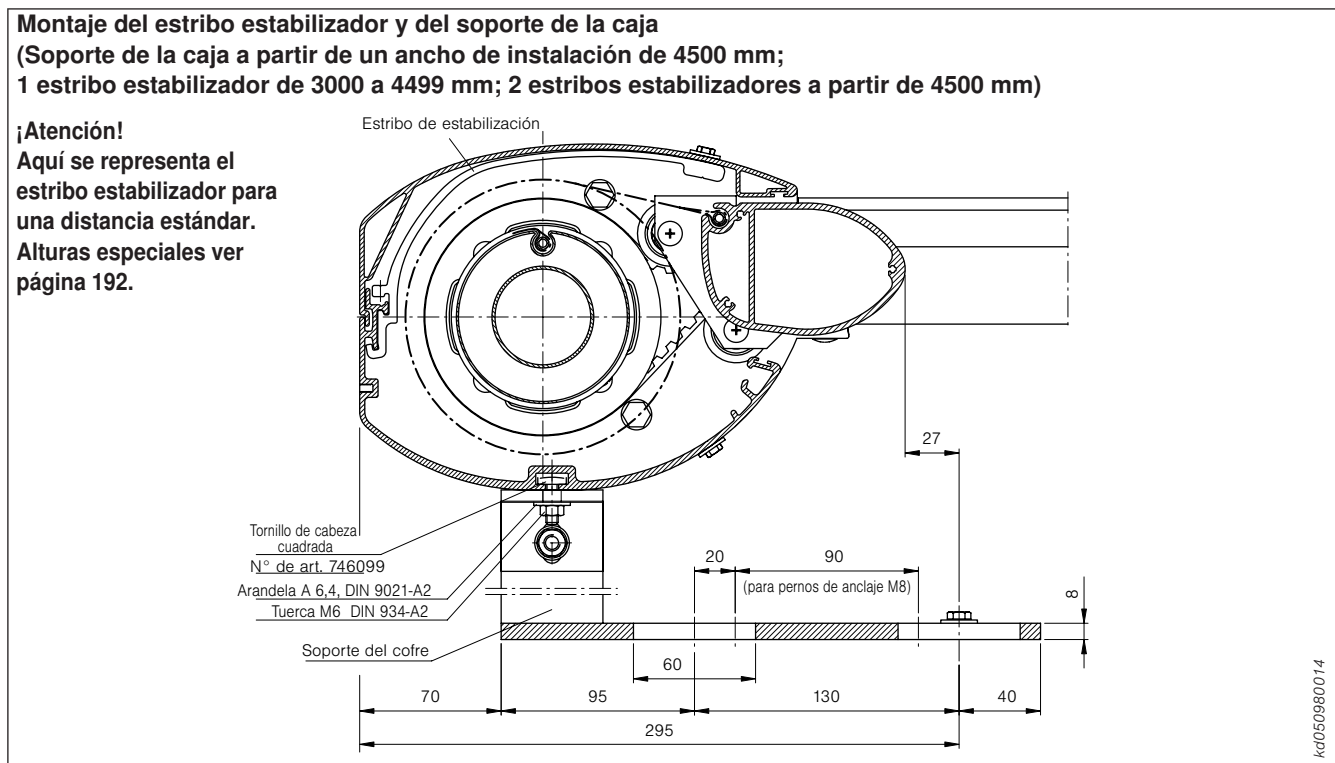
Montaje estribo estabilizador y soporte de la caja
